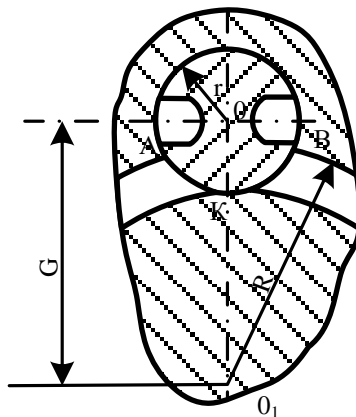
Схема месторасположения ролика-разделителя, ротора и выточки в корпусе
